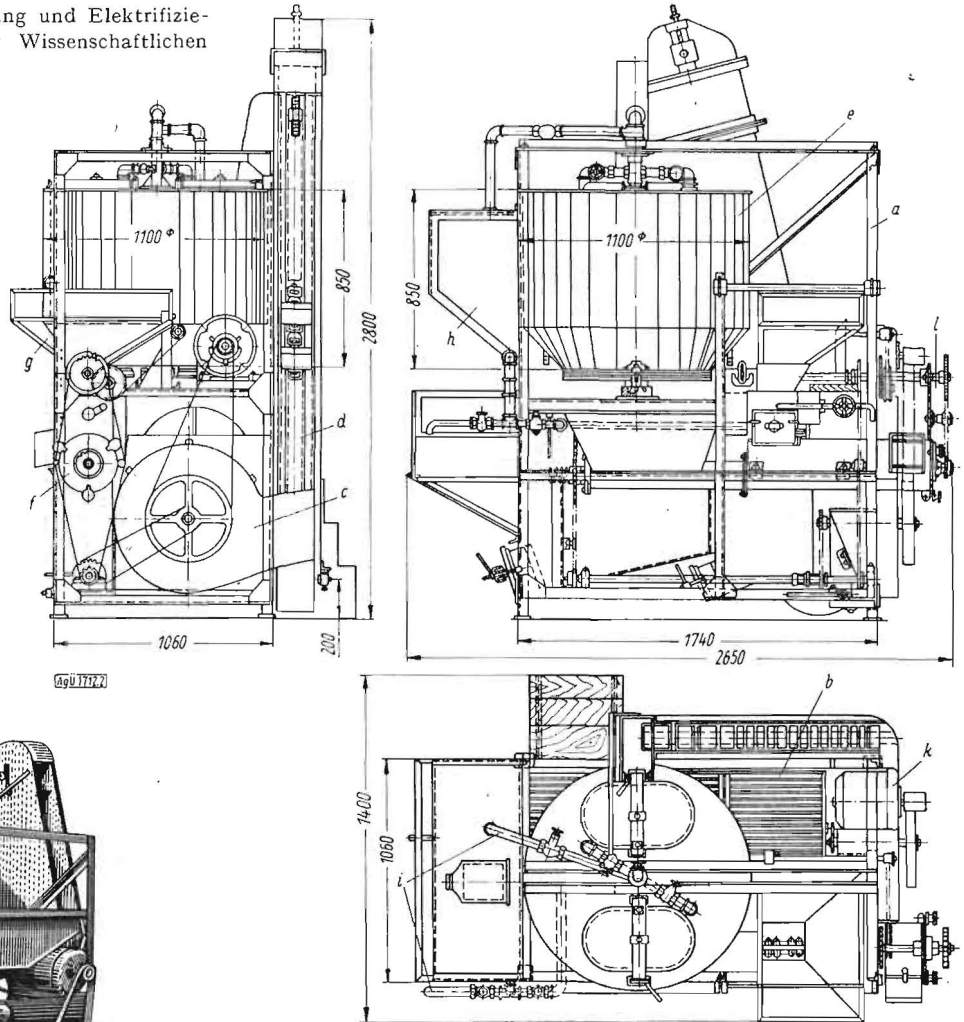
Schema des Futterzubereitungsaggregats: a Rahmen des Aggregats; b Wurzelfruchtwäsche; c Wurzelschneidwerk, d Förderer; e Dämpfbottich; f Quetsch- und Mischapparat; g Dosierer gemahlener Kraftfuttermittel; h Vorwärmer für Wasser oder Magermilch; i Dampf- und Wasserleitungsrohre; k Elektromotor; l Getriebe
